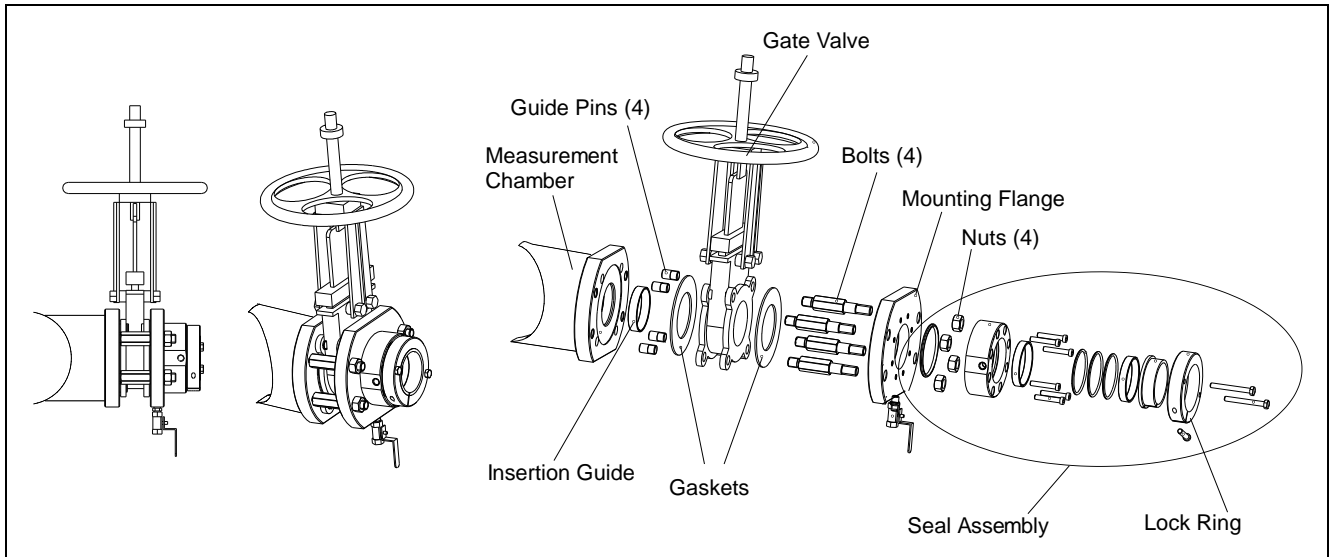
Ensamble adaptador para Adaptador de motaje BTG.
